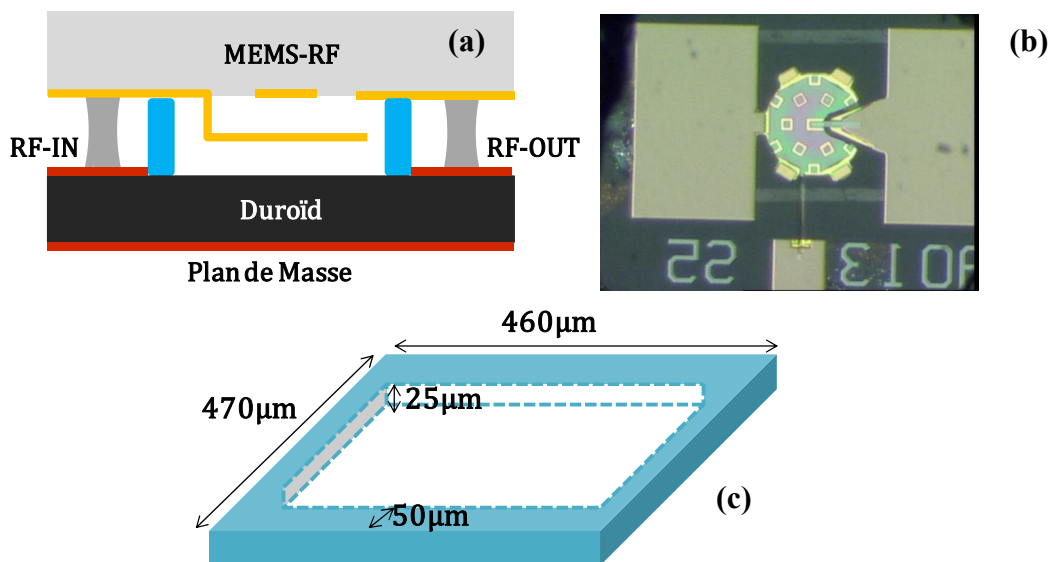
Montage Flip-chip, (a) Vue en coupe, (b) Vue de dessus, (c) Anneau en SU8
